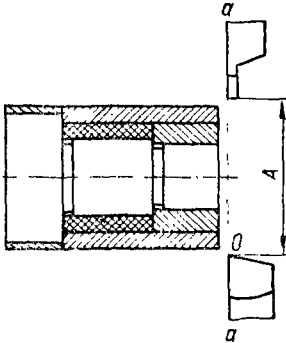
Схема установки резцов на суппорте токарного станка с программным управлением.
